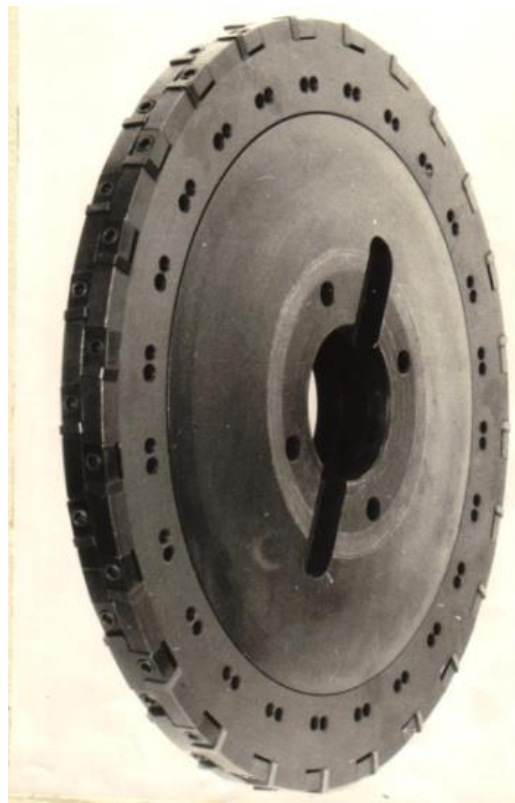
Конструкція дискової фрези двостороннього різання
